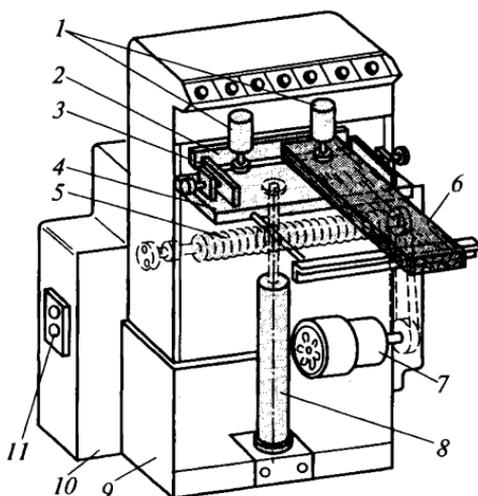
Шипорезный станок для выработки прямых ящичных или клиновых шипов:
